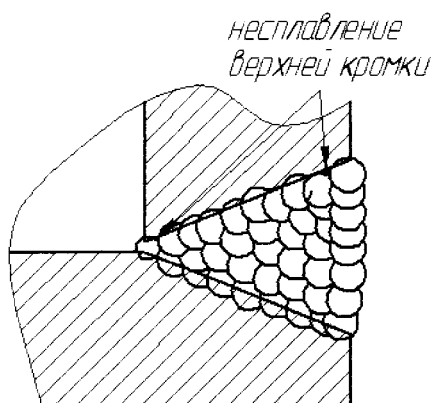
Дефекты, возникающие при сварке горизонтального шва при сварке стенки боковой к корпусу камеры АВО
